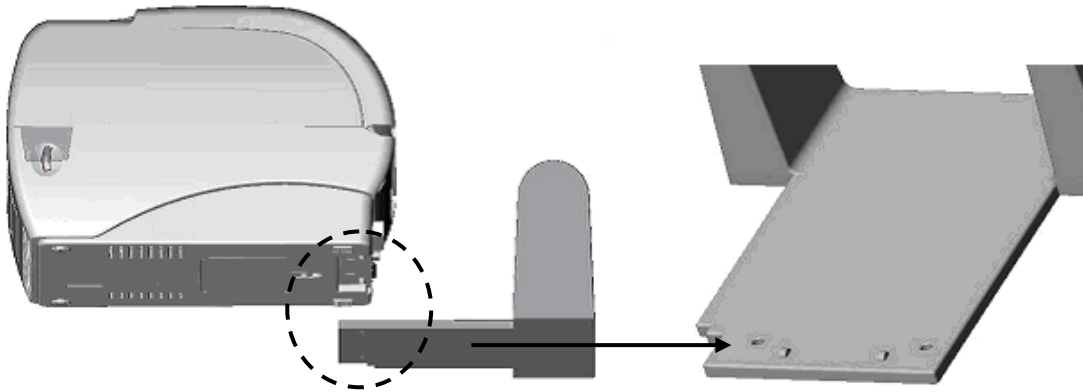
Collegamento della struttura esterna per etichette a bobina alla stampante
